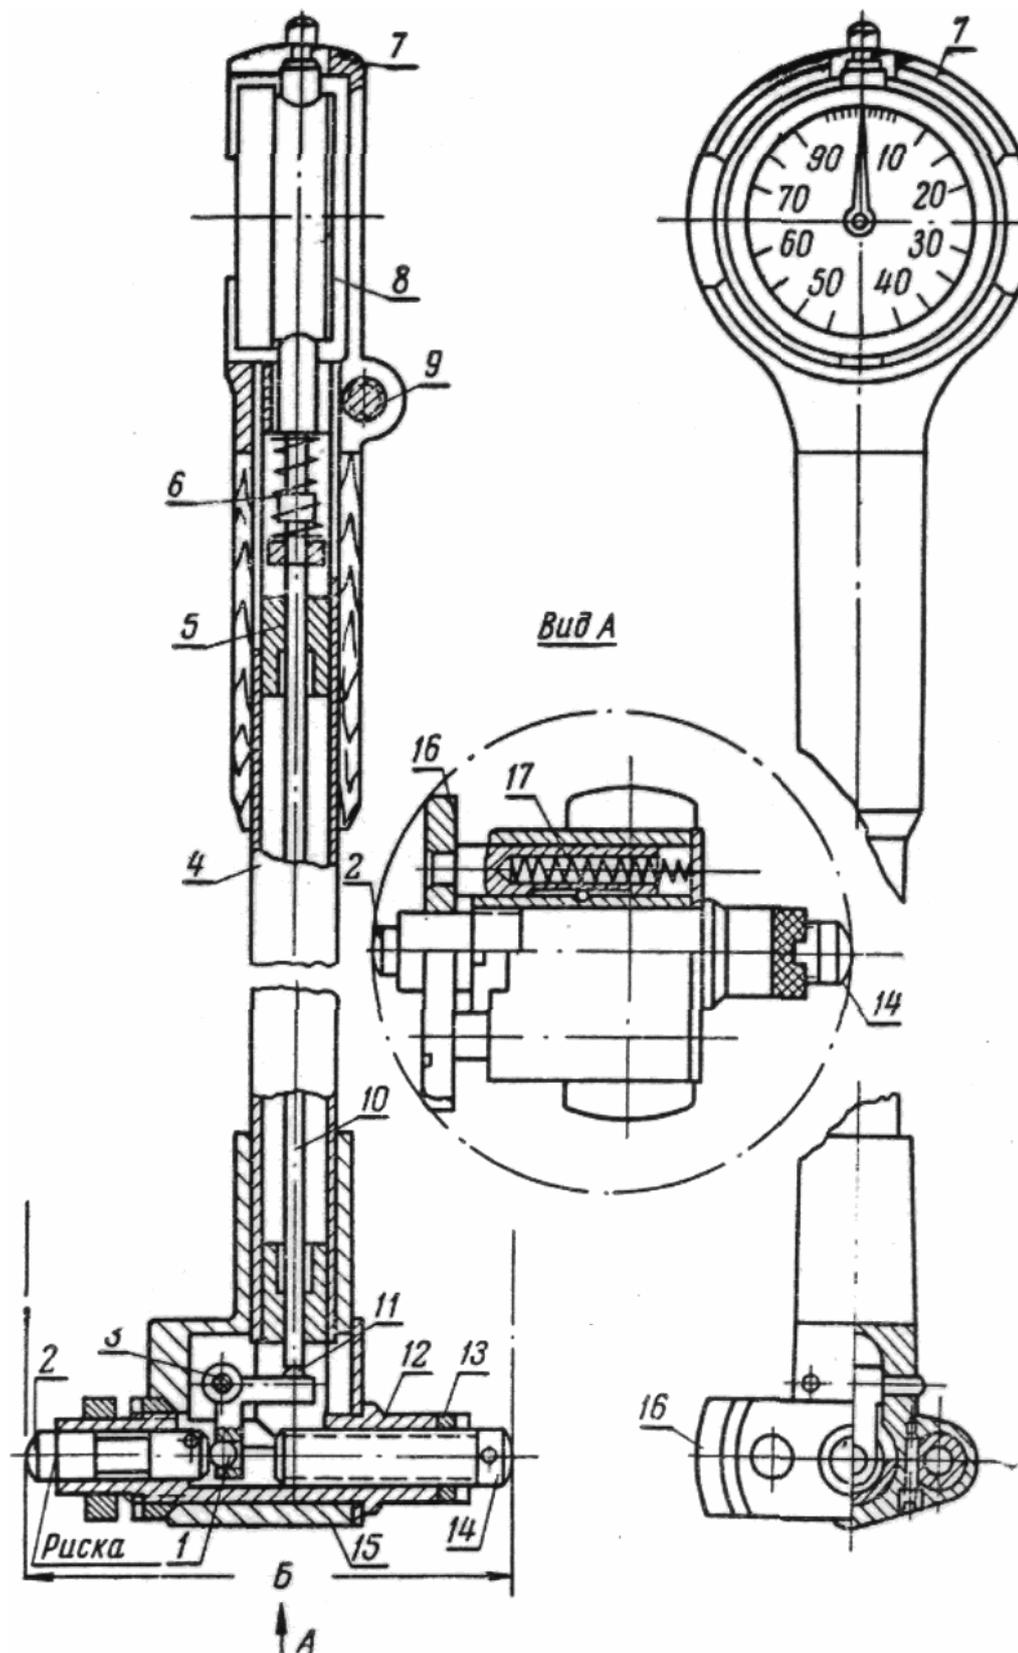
Индикаторный нутромер с рычажной передачей:
